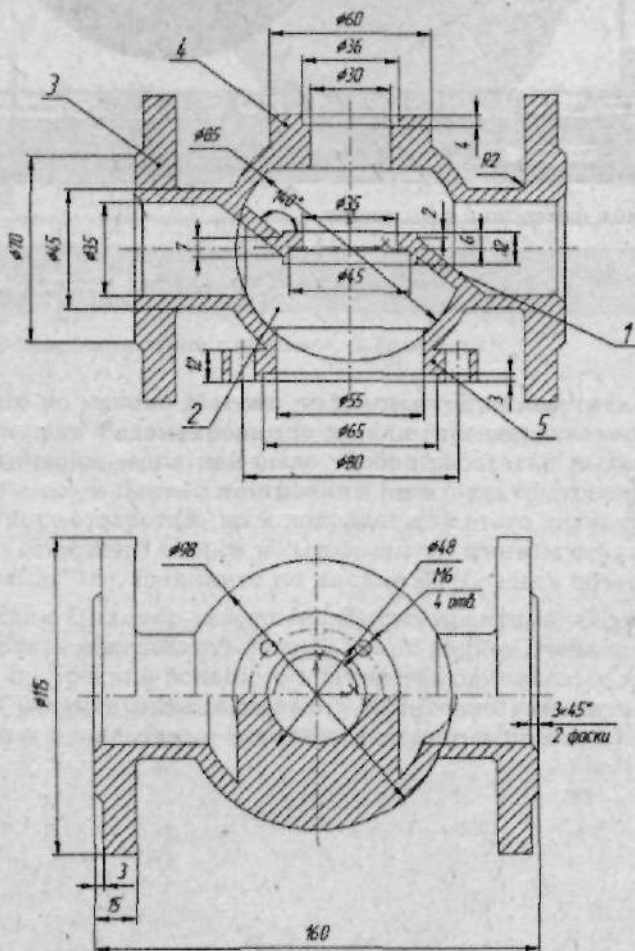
Чертеж детали Корпус (вид спереди, вид сверху)
